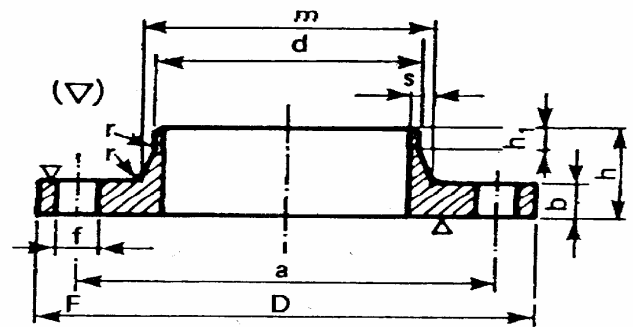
Flangia a collare per tubazioni da saldare di testa.
